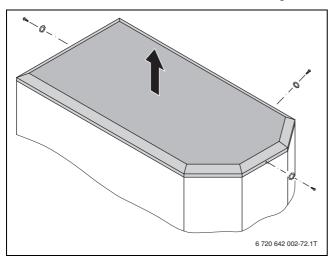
FBP 26-25, FBP 26-32: Deckel demontieren
